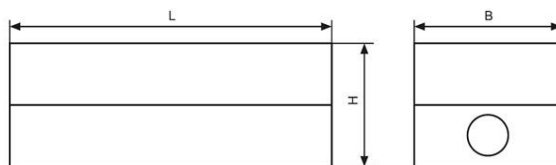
Общий вид и габаритные размеры поста управления кнопочного в пластиковом корпусе
